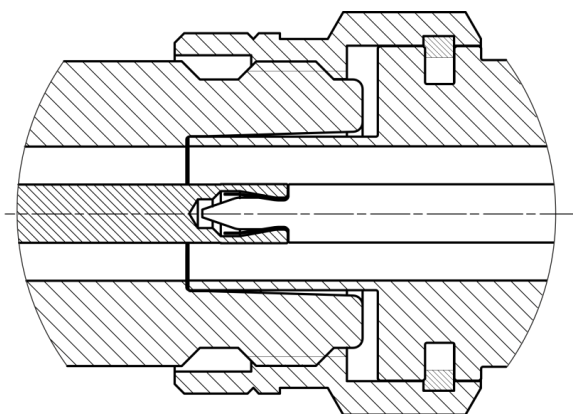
Соединители тип N и III (розетка слева, вилка справа)
